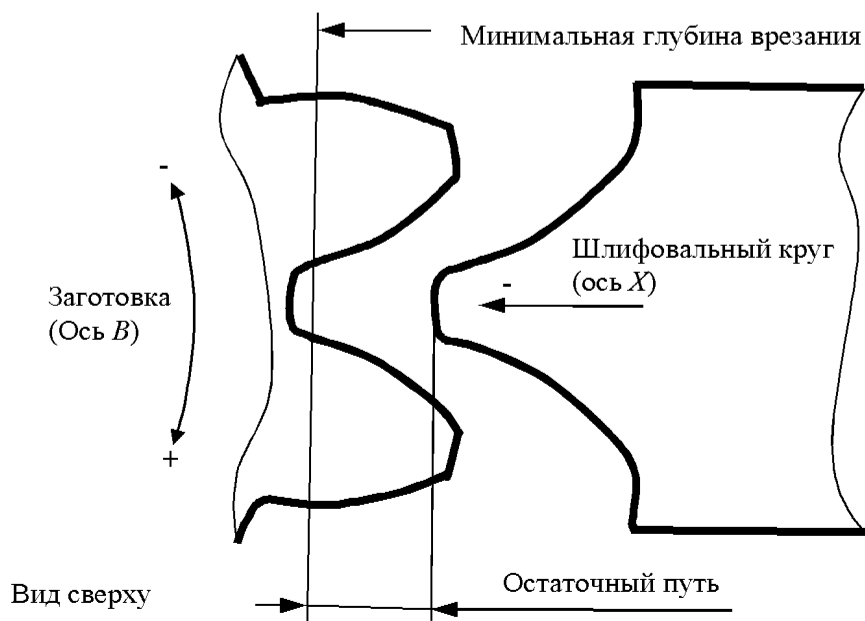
Фрагмент настройки профиля шлифовального круга относительно впадины зубчатого колеса путём чередующихся поворотов заготовки вокруг оси *B
